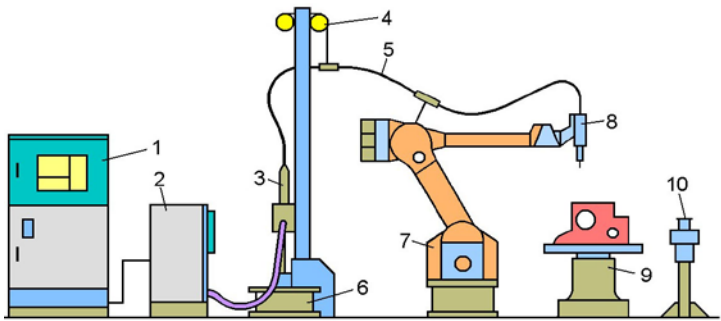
Schweißausrüstung für einen Roboterarbeitsplatz zum MIG/MAG-Schweißen. 1 Robotersteuerung, 2 Schweißgleichrichter, 3 Drahtförder-Vorschubantrieb, 4 Schlauchpaket-Aufhängung, 5 Schlauchpaket, 6 Schweißdrahtgroßspule, 7 Industrieroboter, 8 Brennerkopf mit Drahtförder-Hauptantrieb, 9 Schweißtisch, 10 Brenner-Reinigungsgerät
